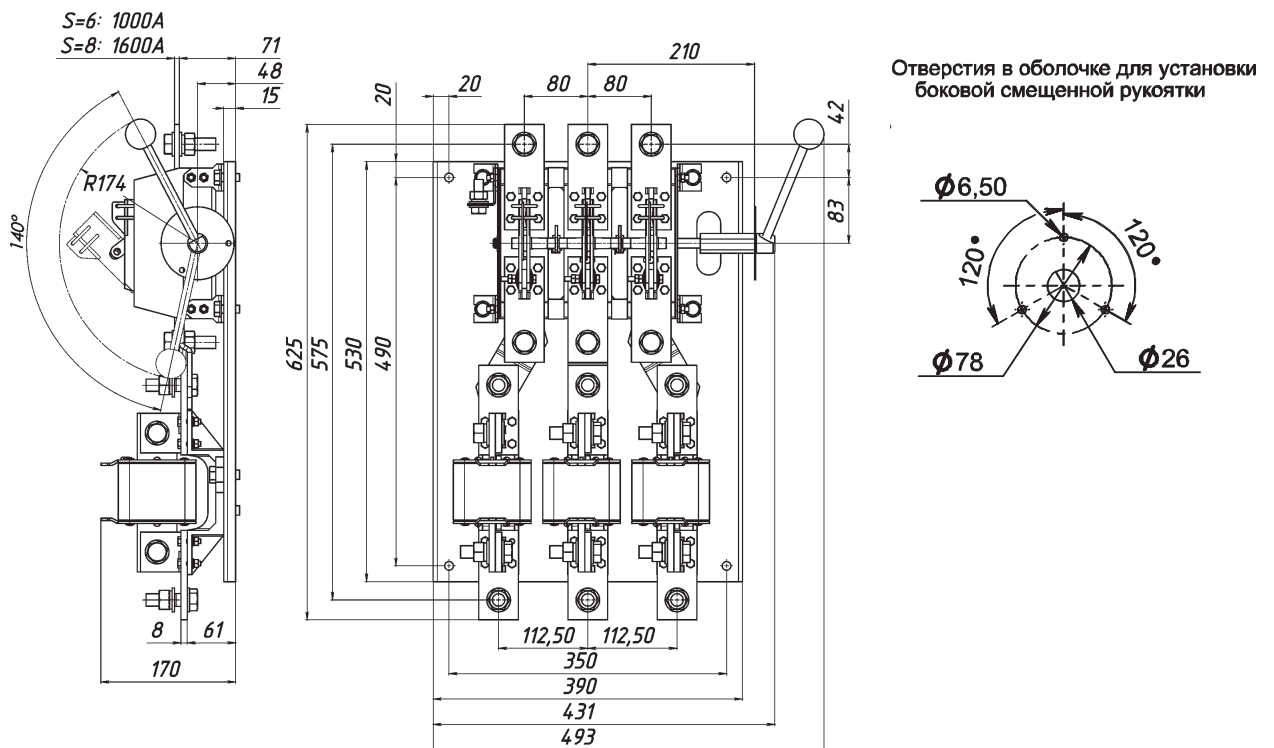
Разъединители-предохранители с боковой смещенной рукояткой на токи 1000 А и 1600 А
